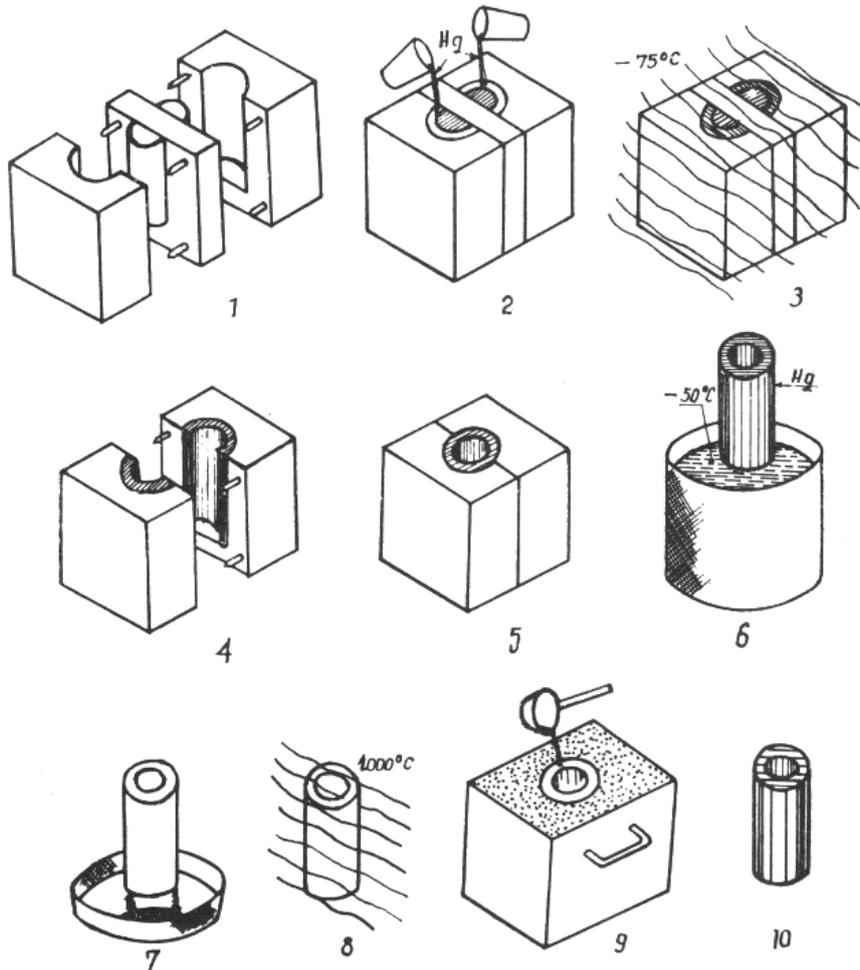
Moldeo por el procedimiento Mercast: 1) coquilla metálica con placa intermedia de machos; 2) colada; 3) enfriamiento de la coquilla a -75° ; 4) separación de las placas intermedias; 5) unión de las dos mitades del molde sin placa intermedia, quedando los modelos de mercurio perfectamente adheridos por simple presión; 6) recubrimiento del modelo de mercurio congelado de un baño de papilla cerámica por inmersión; 7) al elevar a la temperatura ambiente se licua el modelo de mercurio y queda el recubrimiento de cerámica; 8) a continuación se cuece el molde formado por el recubrimiento; 9) colada una vez rodeado el molde de arena para mejorar su resistencia; 10) pieza terminada.
